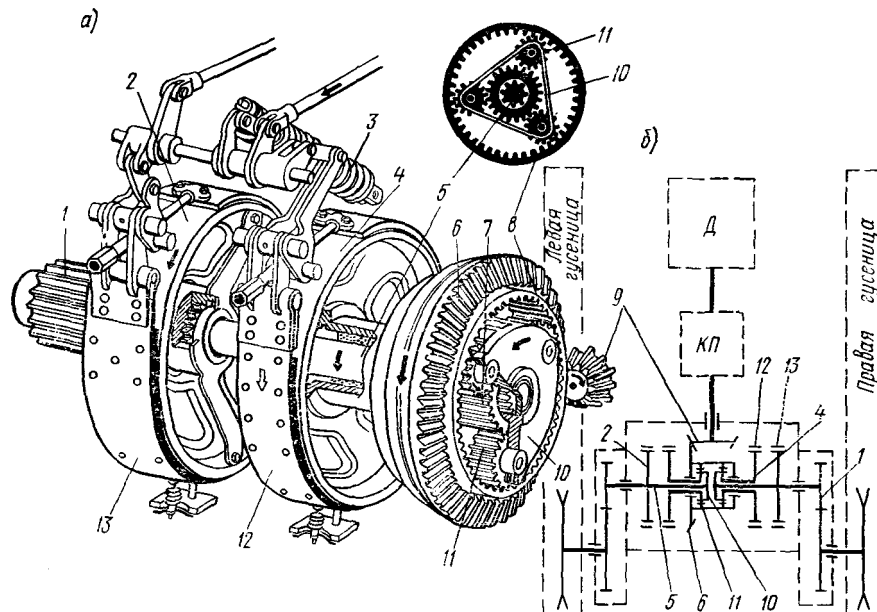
Поворот гусеничного трактора с помощью планетарного механизма:
